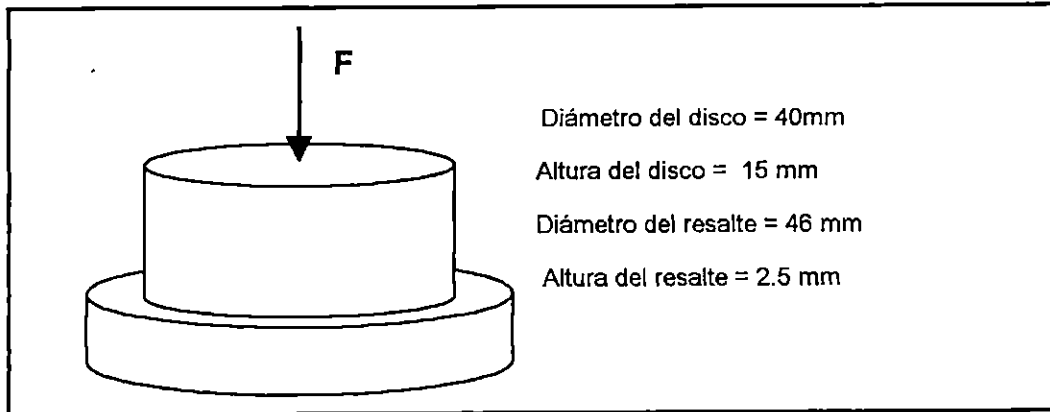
Apoyo superior para la prueba de compresión de materiales.
